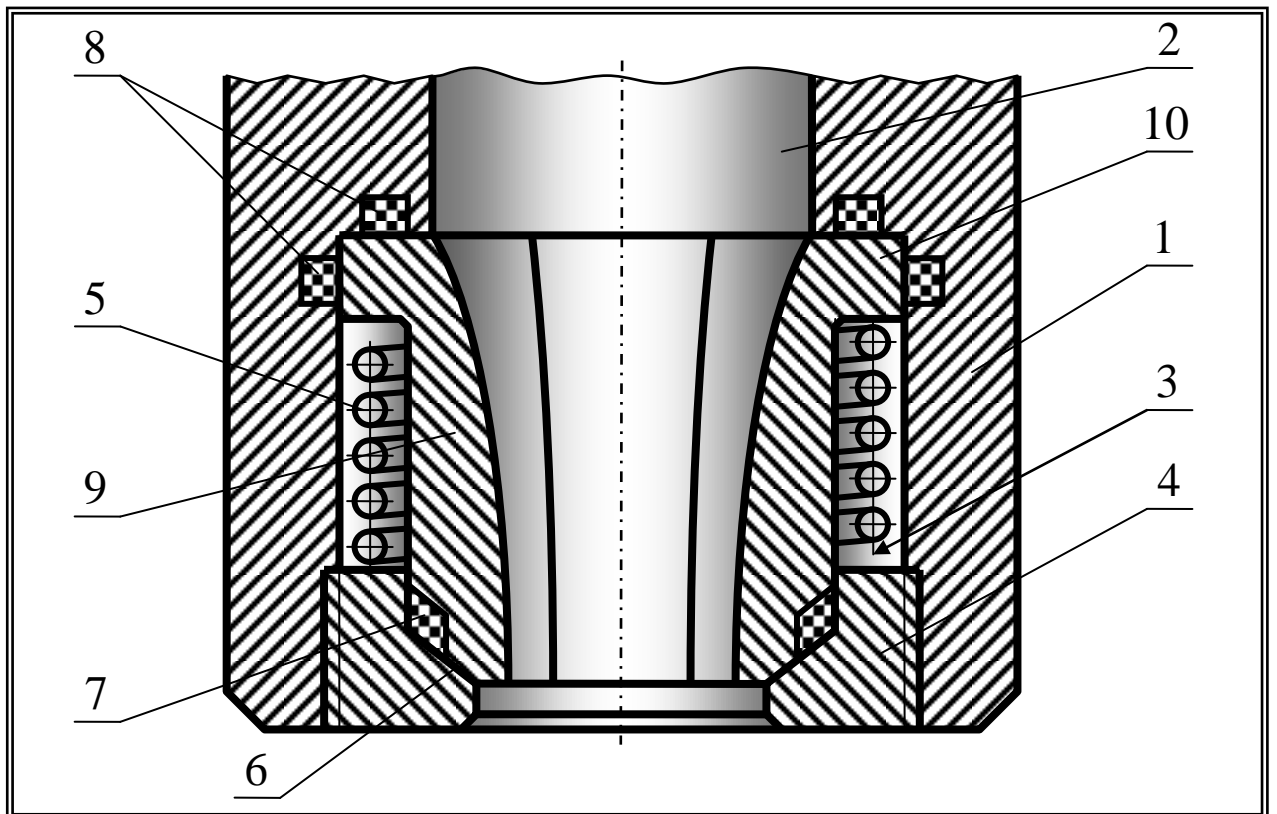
Схема промывочного гидромониторного узла
